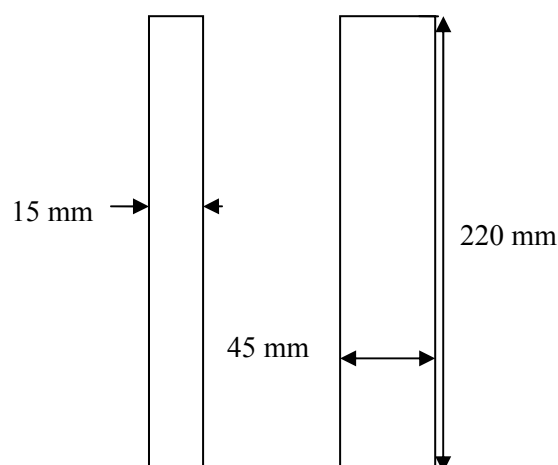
Géométrie des éprouvettes de traction uniaxiale - bois contreplaqué
